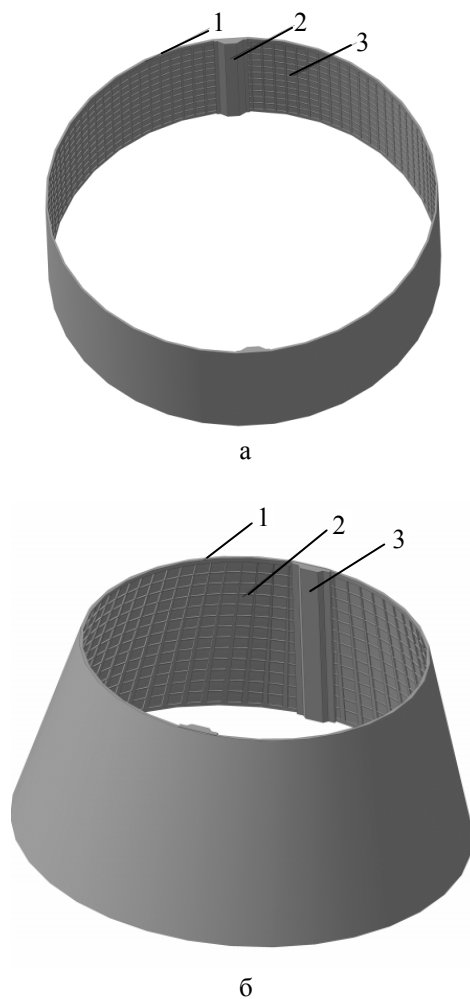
Общий вид цилиндрической (а) и конической (б) обечаек с основными конструкциями и элементами (1 – торцевой шпангоут, 2 – подкрепление оболочки "вафельный фон", 3 – балка функционального стыка)
